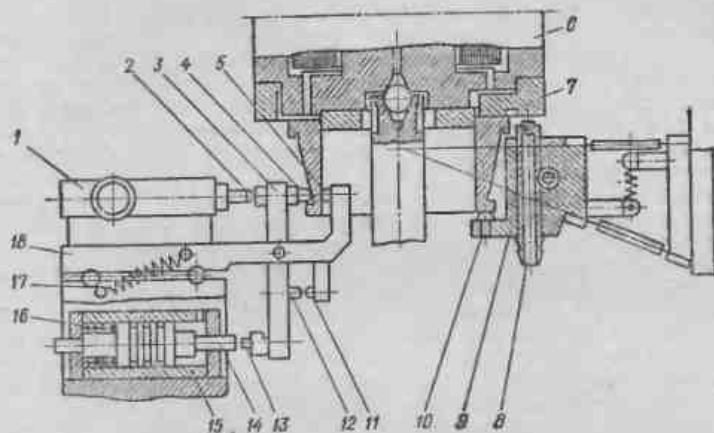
Вторая позиция автомата ЕВ-471 для контроля колец роликоподшипников
